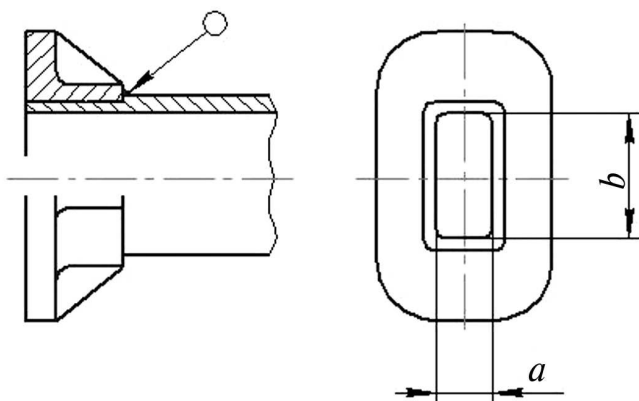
Типовая конструкция сварного соединения трубы и фланца
